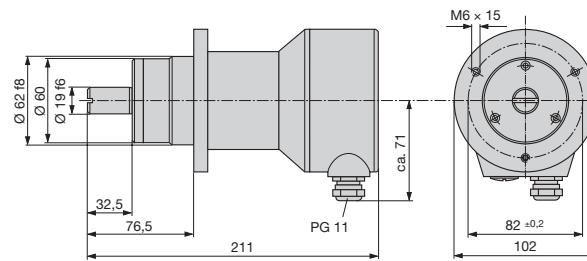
KINAX WT 717 mit Zusatzgetriebe.
